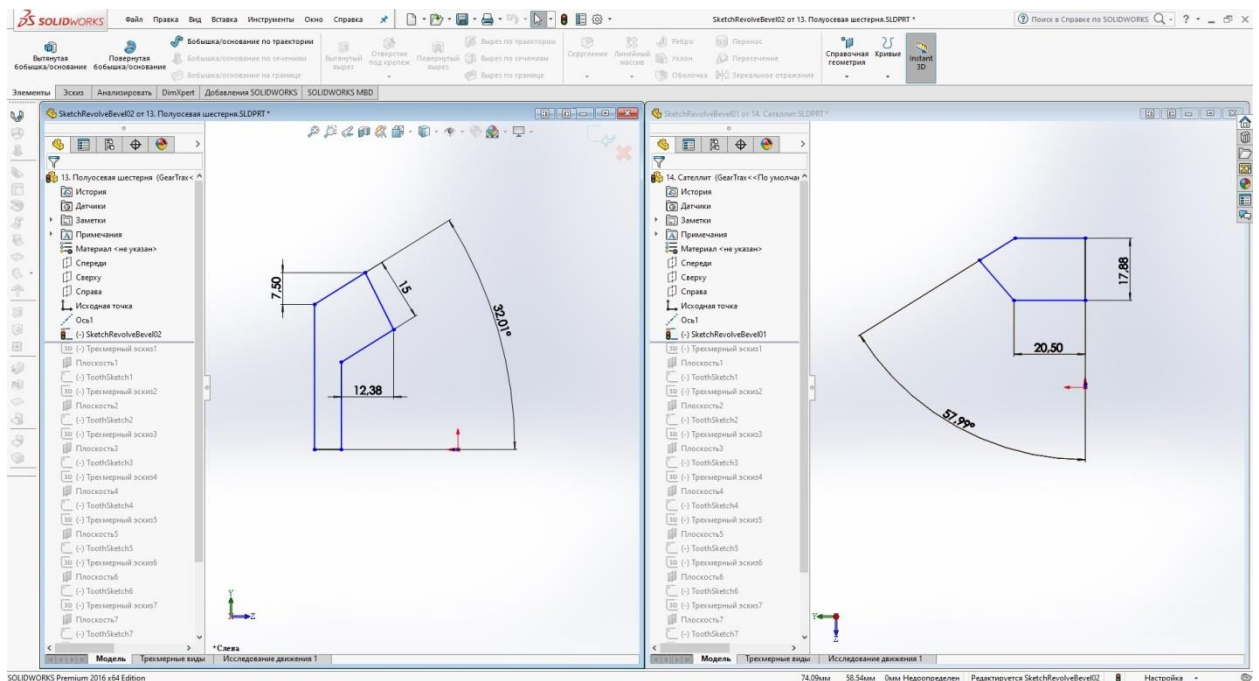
Эскизы полуосевой шестерни и сателлита симметричного конического дифференциала
